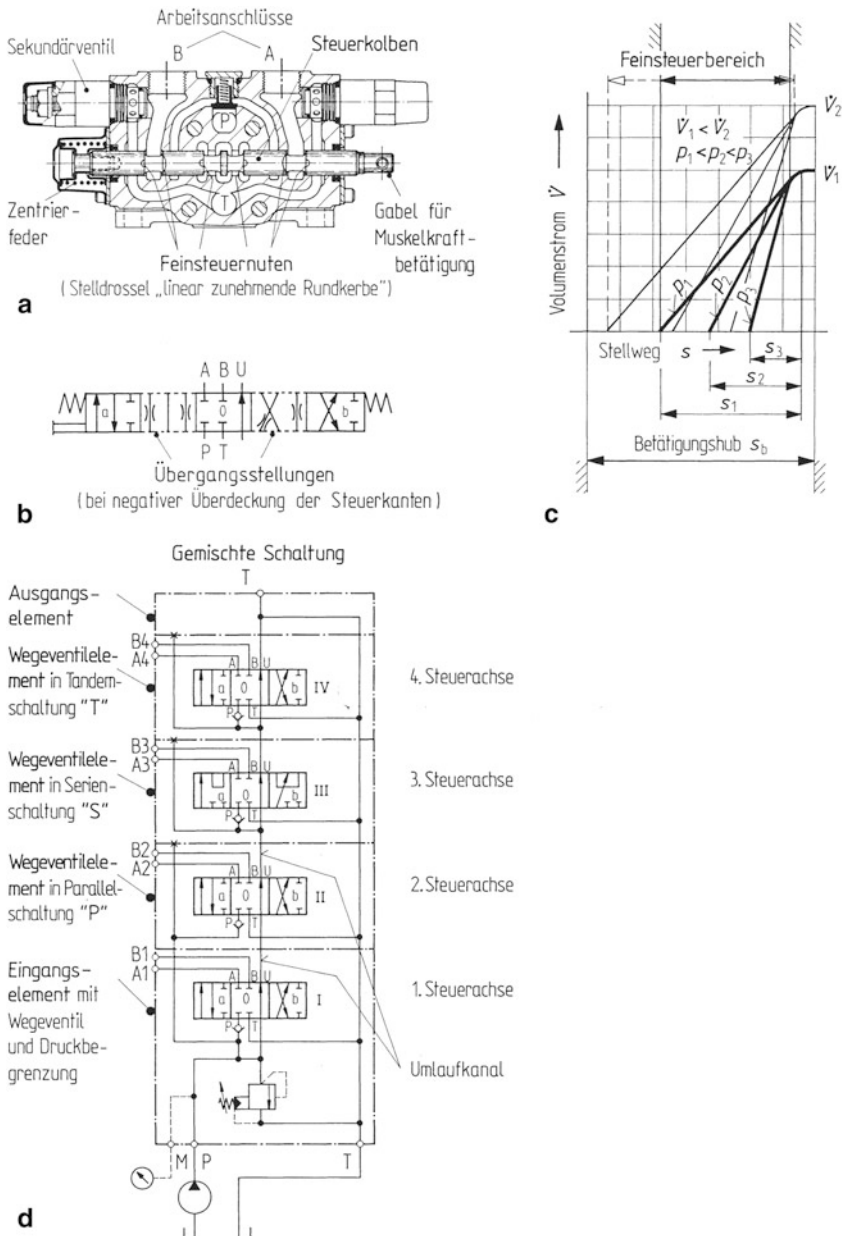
6/3-Wegeventil-Drosselsteuerung. a Wegeventilelement in Tandemschaltung (SM 12, Bosch Rexroth), mechanisch betätigt, Aufbau, Steuerkolben mit optimierten Feinsteuernuten mit Umlaufkanal; b Symbol, Wegeventil mit drosselnder Zusatzfunktion, Durchfluss-Zwischenstellungen (negative Überdeckung) zwischen 3 Schaltstellungen; c lastdruckabhängige Ventilkennlinie (Wirkprinzip „Drosselsteuerung“); d gemischte Schaltung eines Wegeventilblocks für Konstantpumpe mit Neutralumlauf (Open Center), lastdruckabhängig, vier Verbraucher (Steuerachsen)
